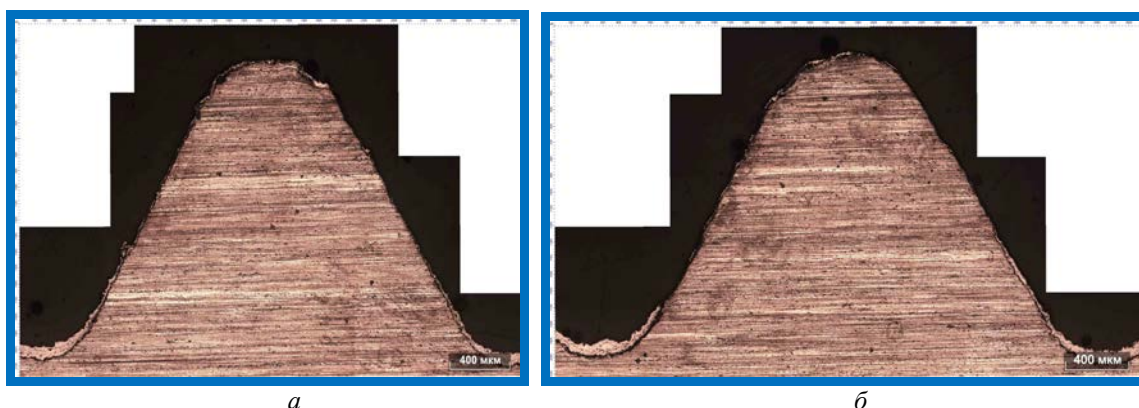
Вид профиля резьбы, покрытой медью, до (а) и после (б) испытаний
